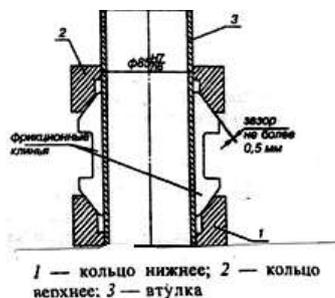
Приспособление для комплектации клиньев буксового гасителя
